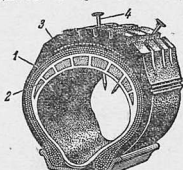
Покрышка с камерой, имеющей ячейки: 1—камера, 2—ячейки, 3—покрышка, 4—гвоздь
